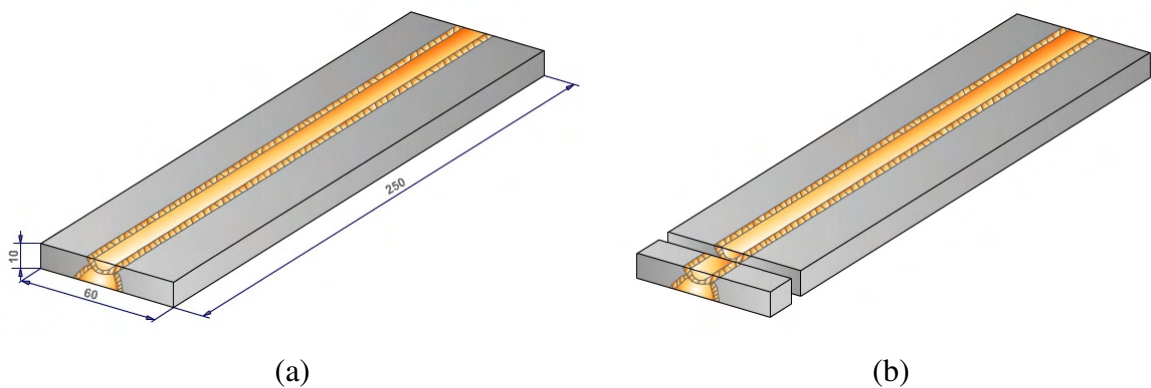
Representação esquemática da junta soldada (a) após retirada do material excedente; (b) seccionada de modo a retirar os corpos-de-prova para o ensaio Charpy.
